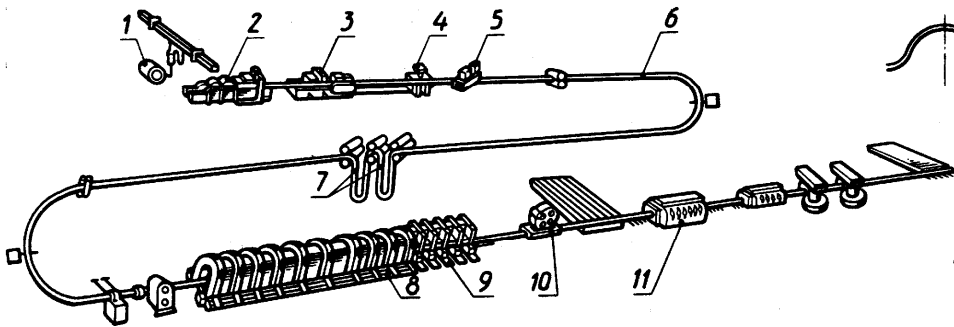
Схема технологического процесса изготовления труб методом непрерывной печной сварки
